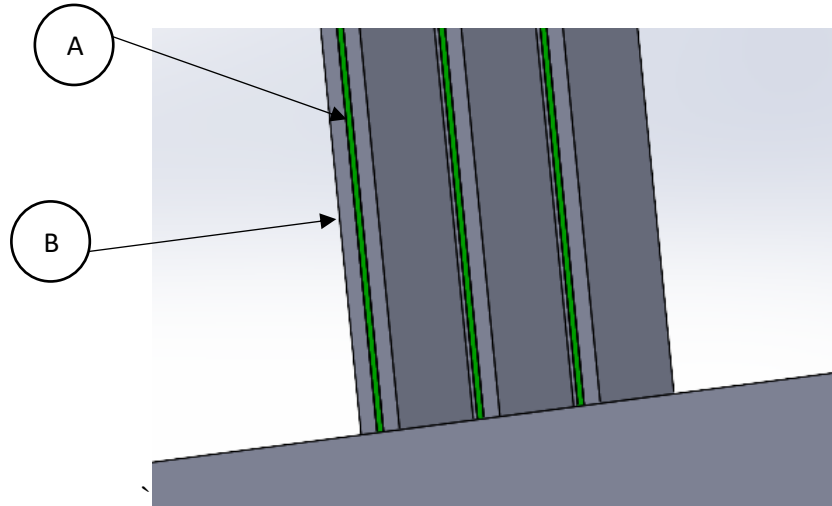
(a) Ilustrasi Sistem Massa *Cantilever-Beam* Piezoelektrik kolom tampak depan
